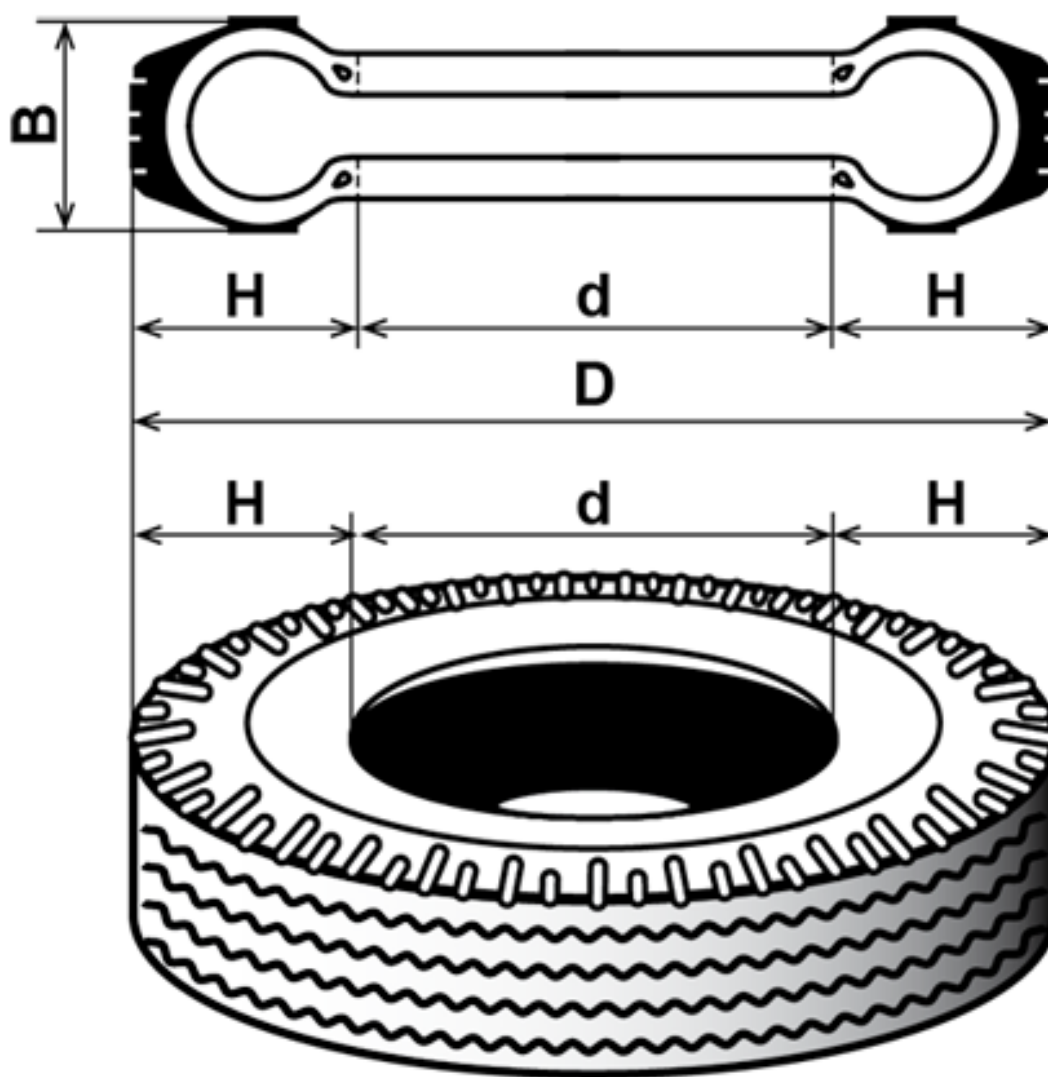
Обозначение размеров шины: В – ширина профиля; d – посадочный диаметр; H – высота профиля; D – наружный диаметр
